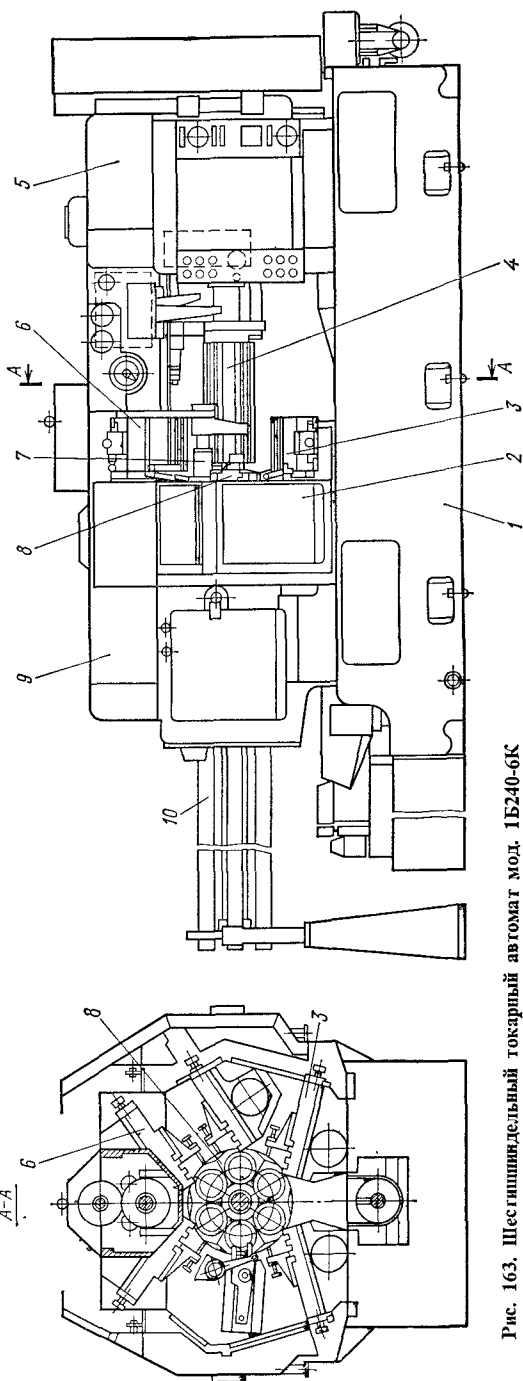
Шестিশпиндельный токарный автомат мод. 1Б240-6К
